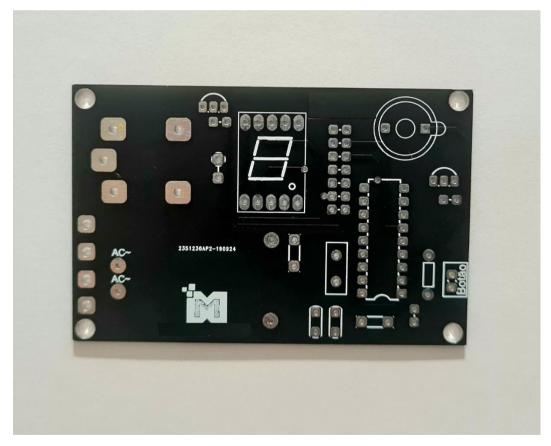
Placa projetada pelo fabricante de circuito impresso Fonte: Autor
